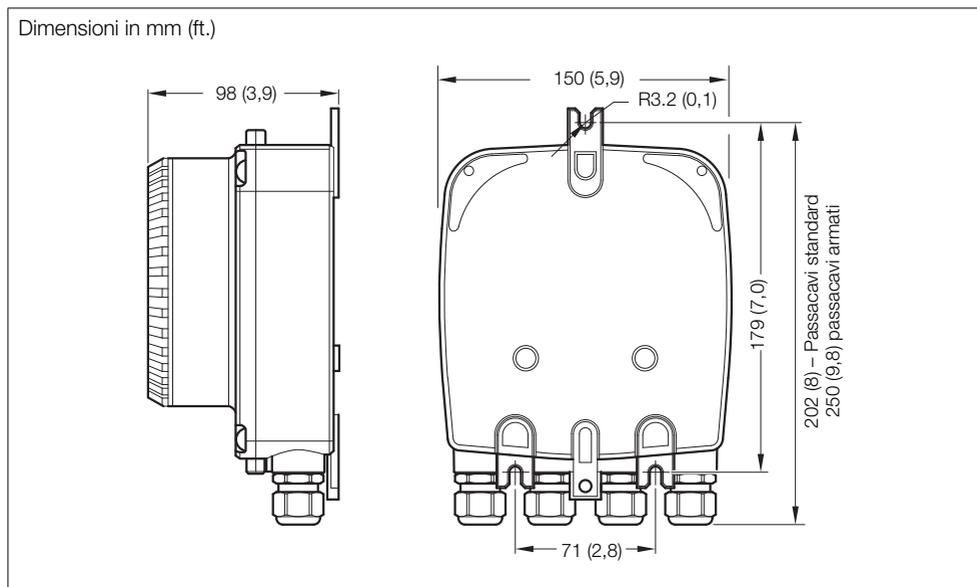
Dimensioni del trasmettitore remoto (passacavo standard in figura)
